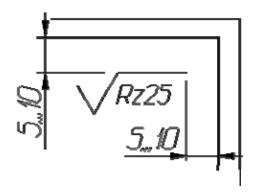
Указание шероховатости одинаковой для всех поверхностей изделия
